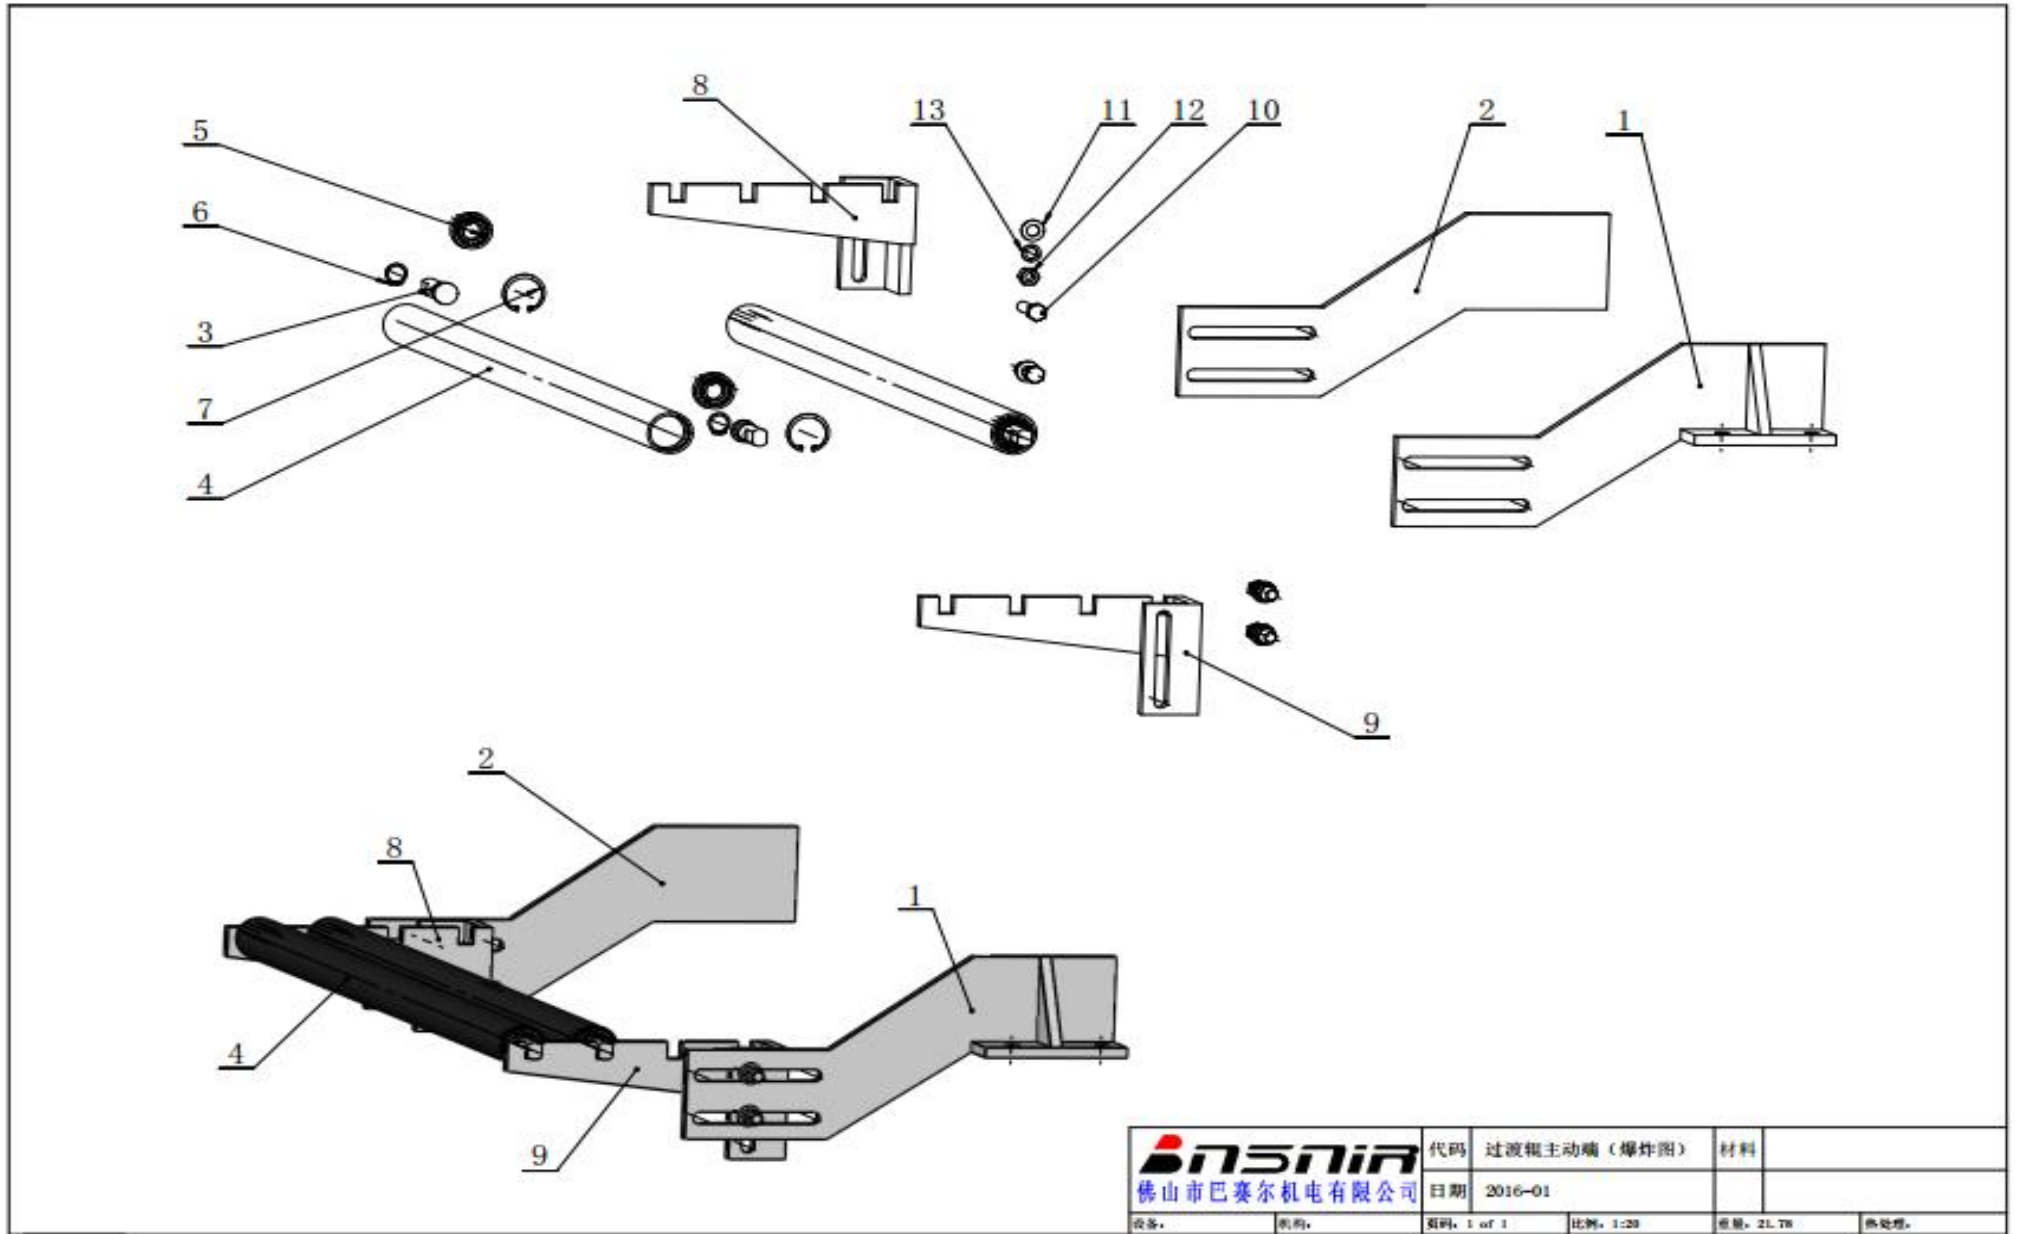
2 机架部分—过渡辊主动端装配图 picture2-2 Gantry parts-the active end assembly of the transition roll
